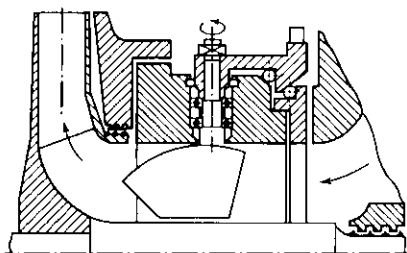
Поворотный лопастный аппарат для закручивания потока перед рабочим колесом при регулировании центробежного компрессора
